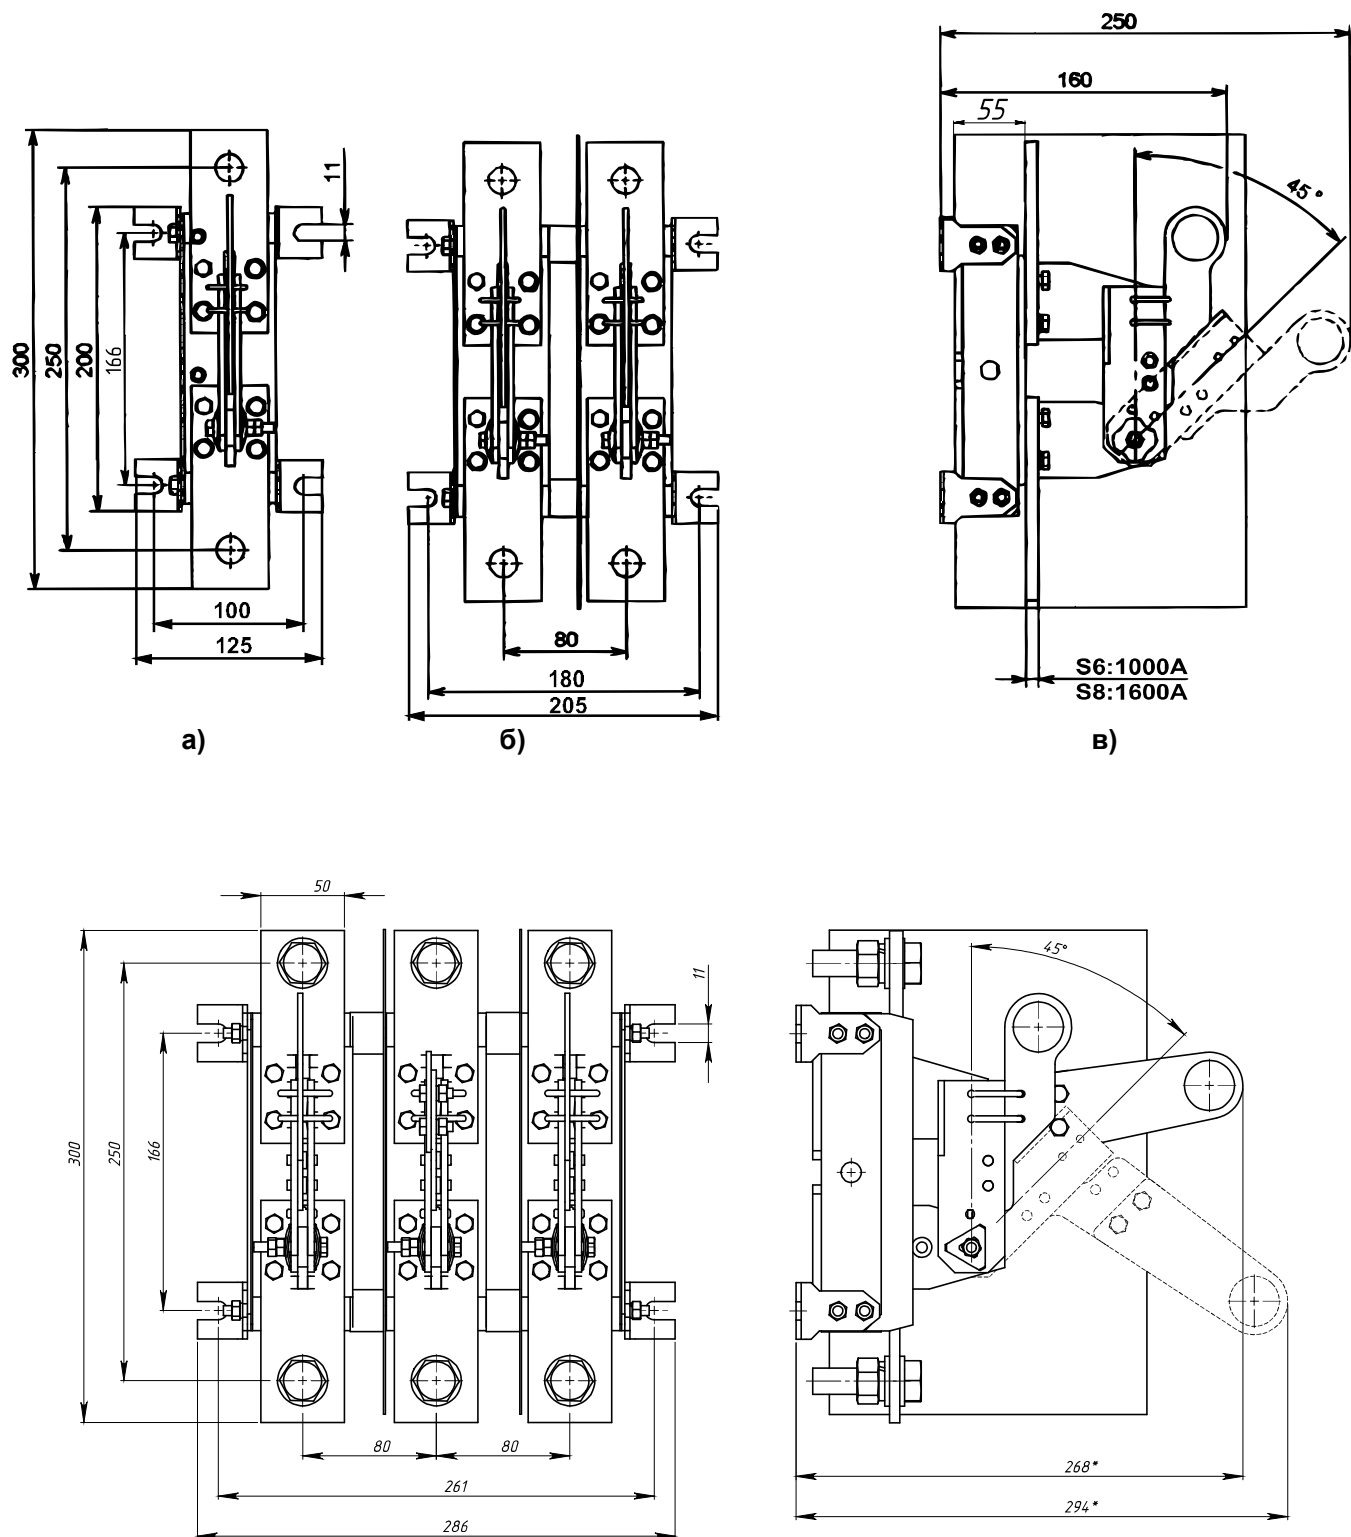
Разъединитель PE19 с рычагом для полюсного оперирования штангой
